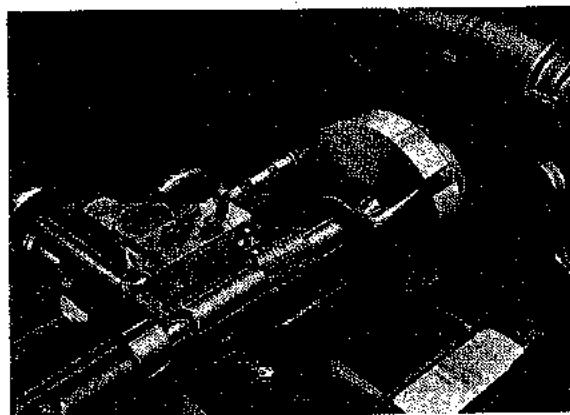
Aparato para destalonar (American Tool Works Co.)
